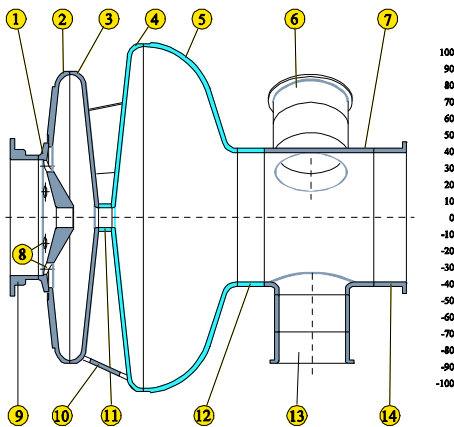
Сверхпроводящий узел: 1 - бобышка, 2-5 - стенки, 6,7,9,12-14 - патрубki, 11 - трубка, 8 - отверстия (6 шт.).
